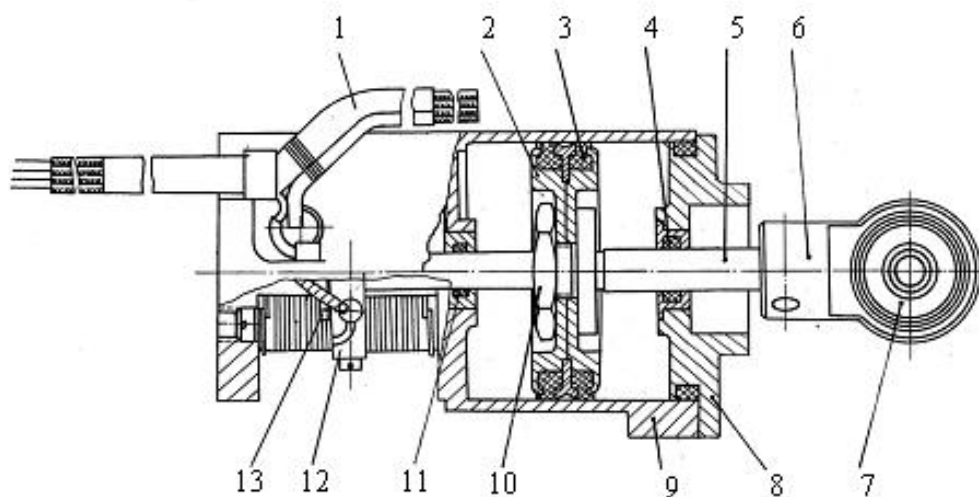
Рулевая машина: 1 – электрожгут; 2 – диск; 3 – резиновая манжета; 4, 11 – уплотнительные кольца; 5 – шток; 6 – серьга; 7 – подшипник; 8 – крышка; 9 – корпус; 10 – гайка; 12 – потенциометр обратной связи; 13 – контактная пластина; 14 – движок потенциометра
